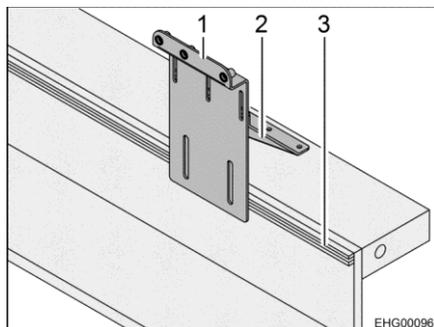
Supporto per la ruota di scorta (sui guida di ancoraggio)
